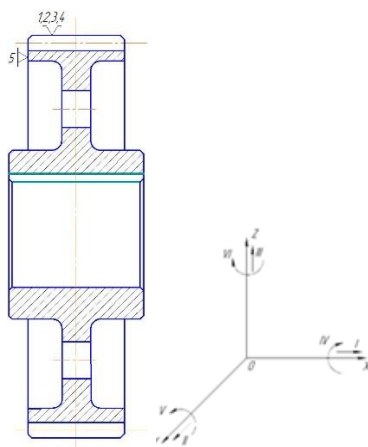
Схема базування заготовки на горизонтально-протяжній операції
